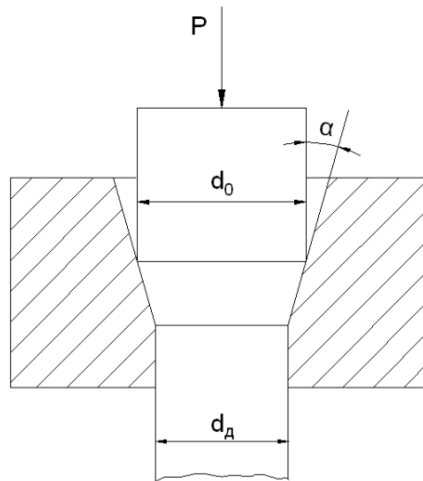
Схема редуцирування циліндричної заготовки в жорсткій конічній матриці
